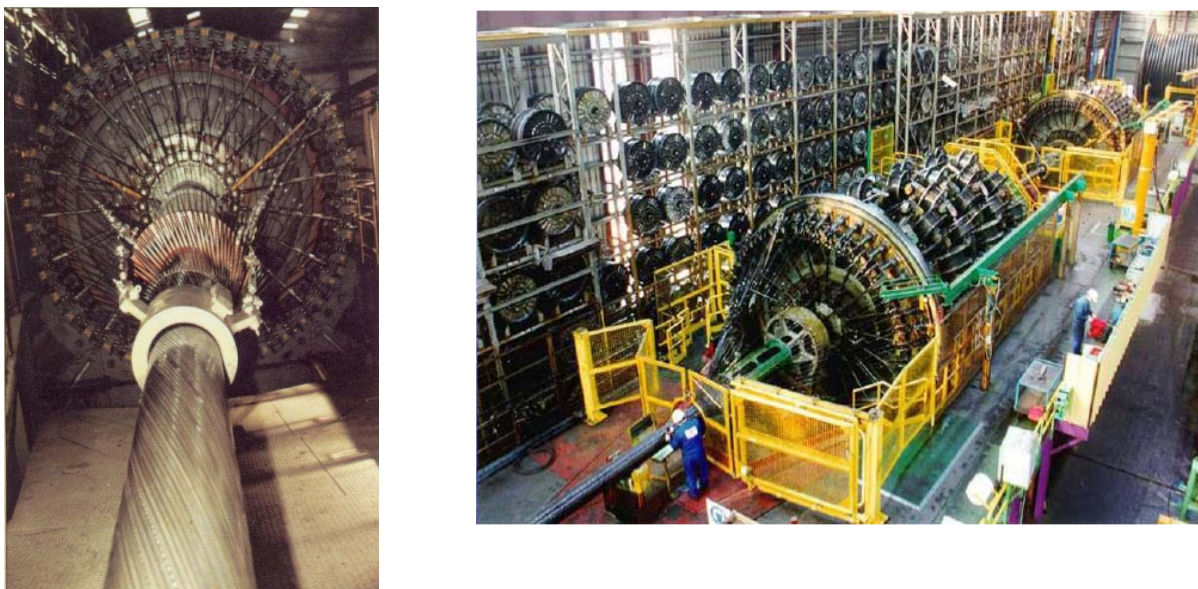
Bobina de assentamento das armaduras de tração (Petrobras)
